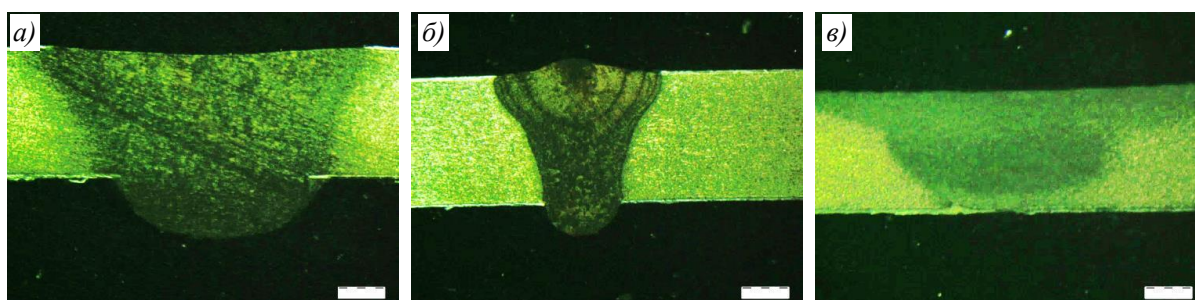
Макроструктура сварных образцов, выполненных автоматической аргоно-дуговой электросваркой (а), лазерной сваркой (б) и сваркой трением с перемешиванием (в)
